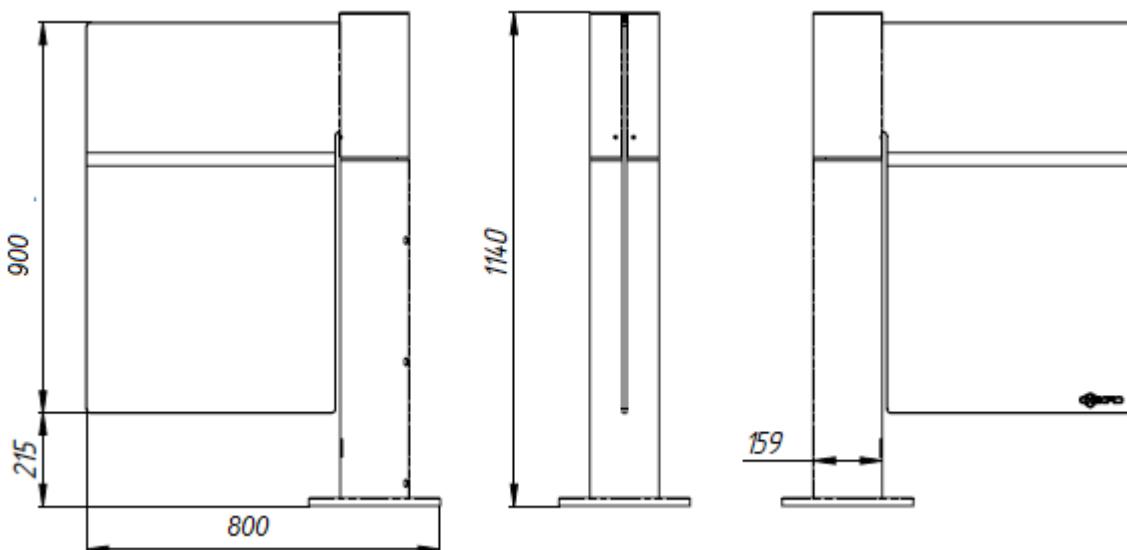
Габаритные размеры калитки шириной прохода 600 мм
